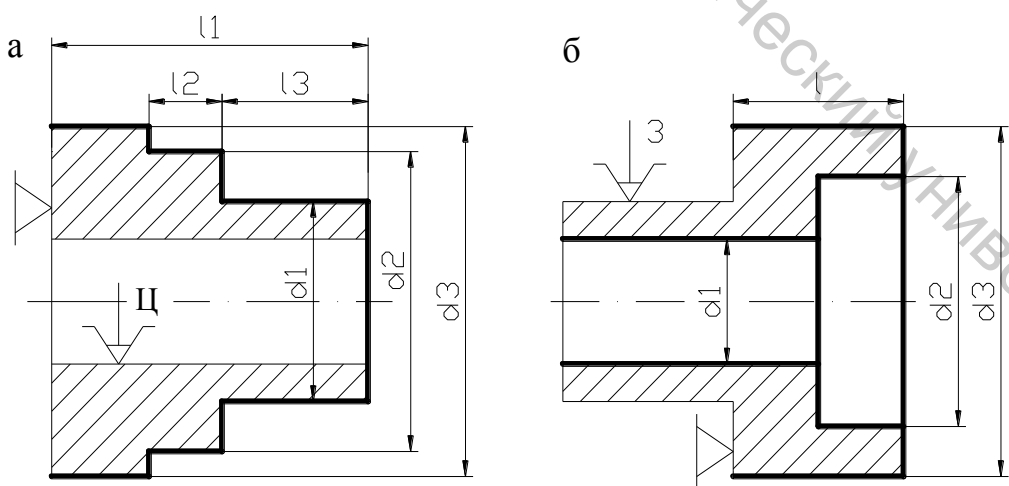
Схемы установки цилиндрических заготовок:
